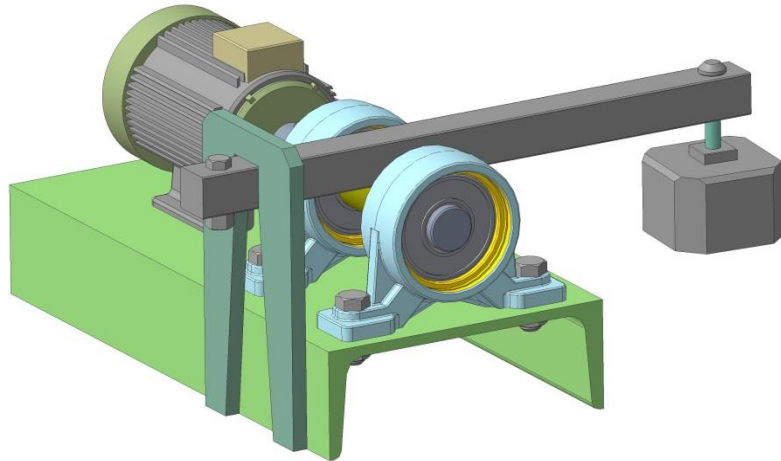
Конфігурація апарату для перевірки кулькових підшипників: 1 - конструкція; 2 - вимірювач шуму; 3 - кульковий підшипник; 4 - база для підшипника; 5 - проміжна ось; 6 - сполучна муфта; 7 - двигун 4АМА71А.
